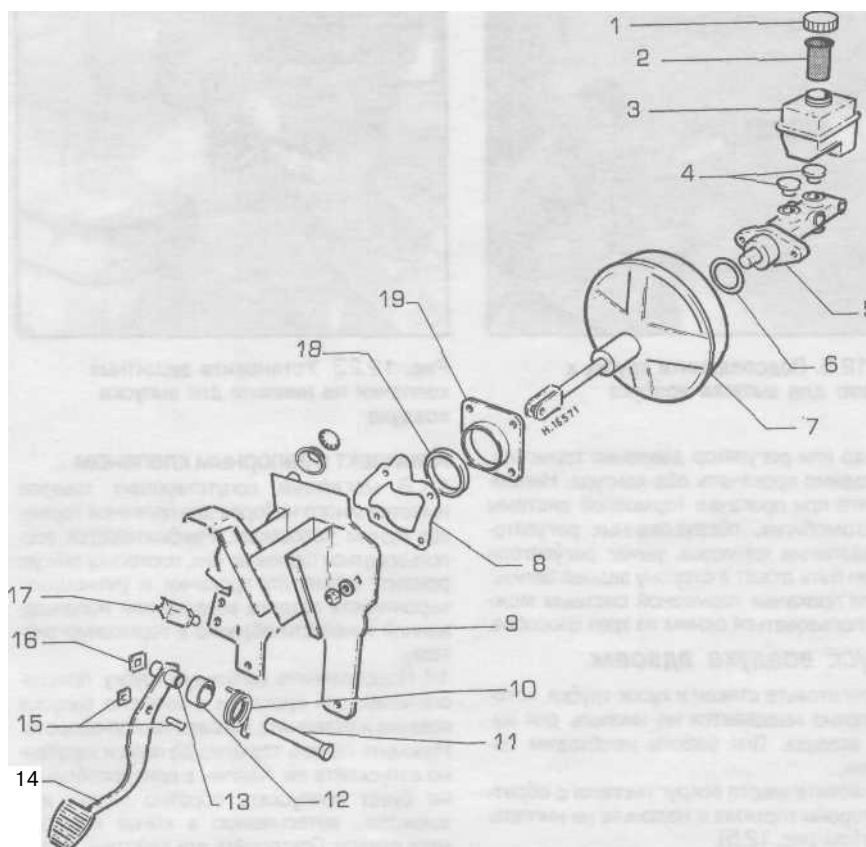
Педаль тормоза, вакуумный усилитель тормозов и главный тормозной цилиндр
